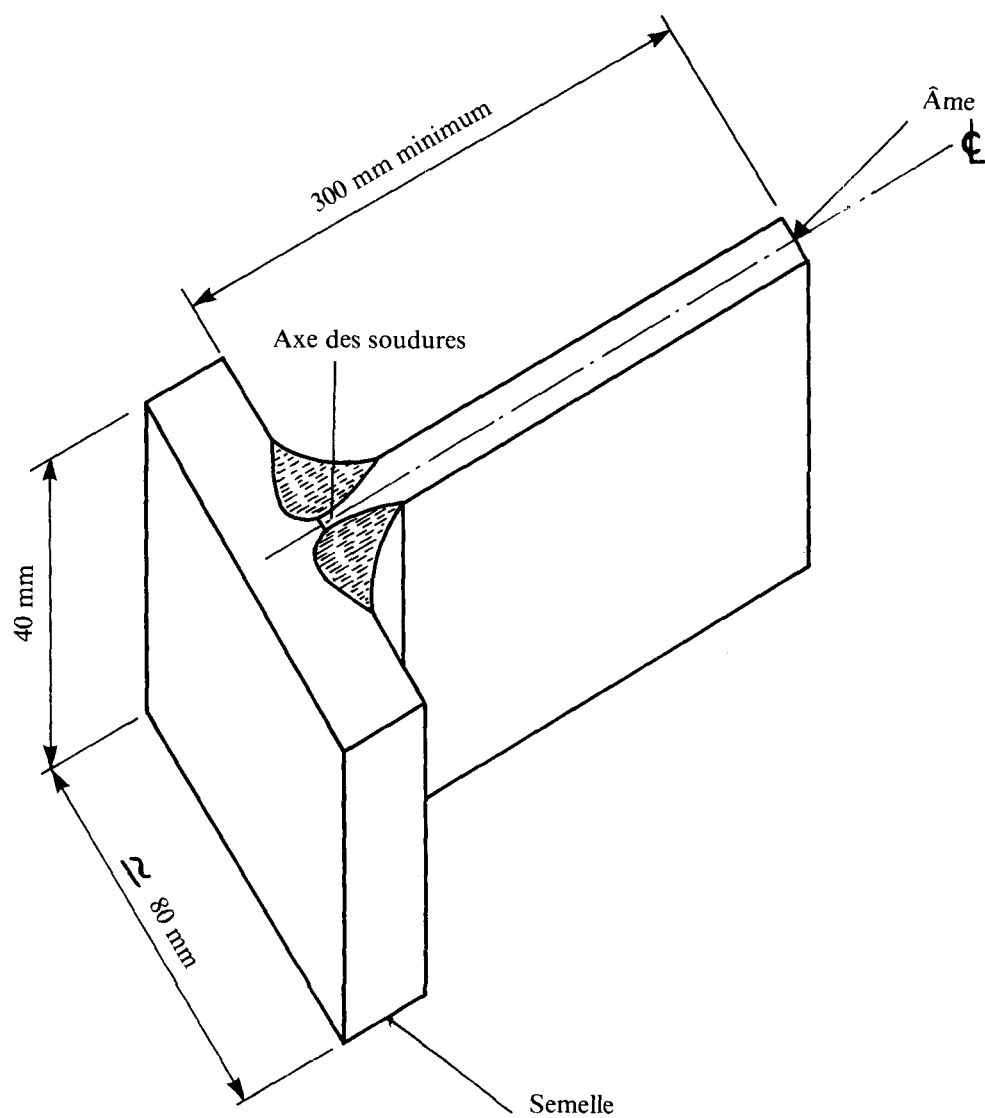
Spécimen pour essai de traction sur soudures d'angle
